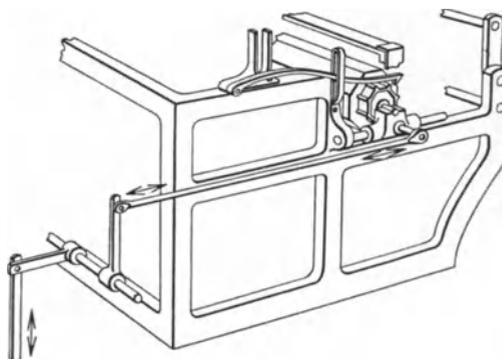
Schema einer Prismenschaltvorrichtung mit Hakensteuerung.
